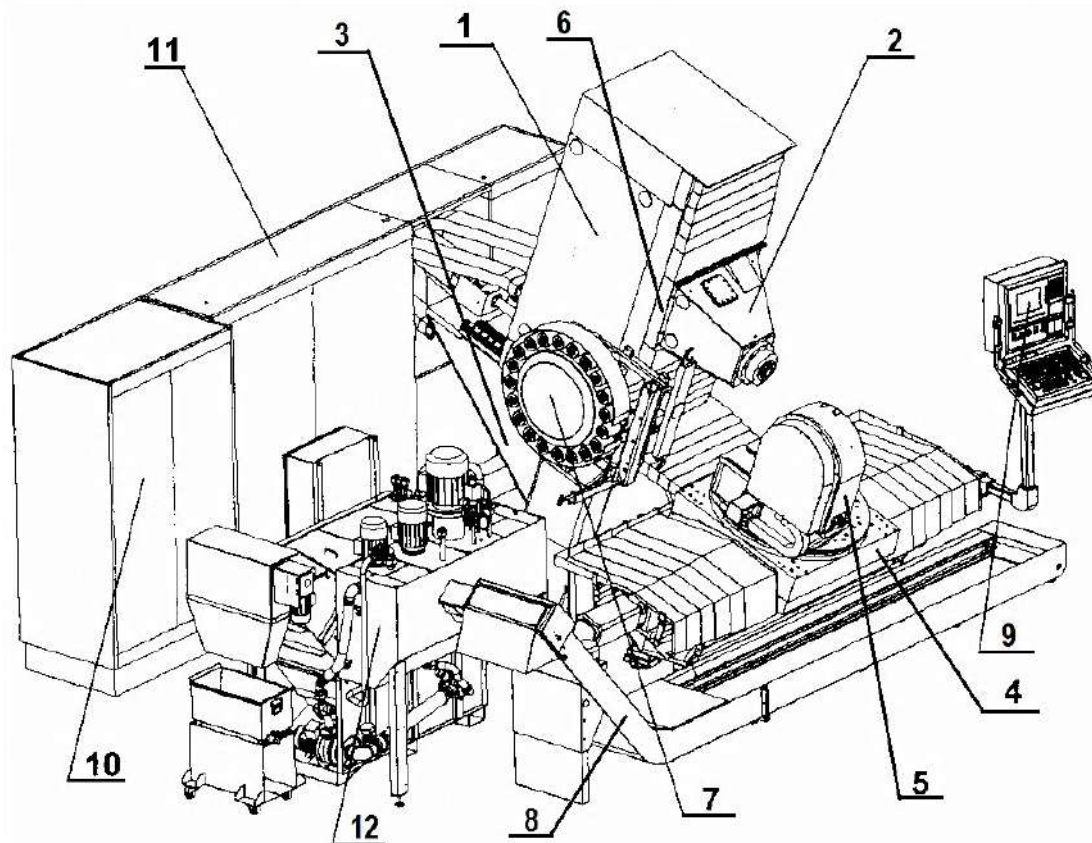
Багатокоординатний фрезерний верстат TURBOBLISK 1005
